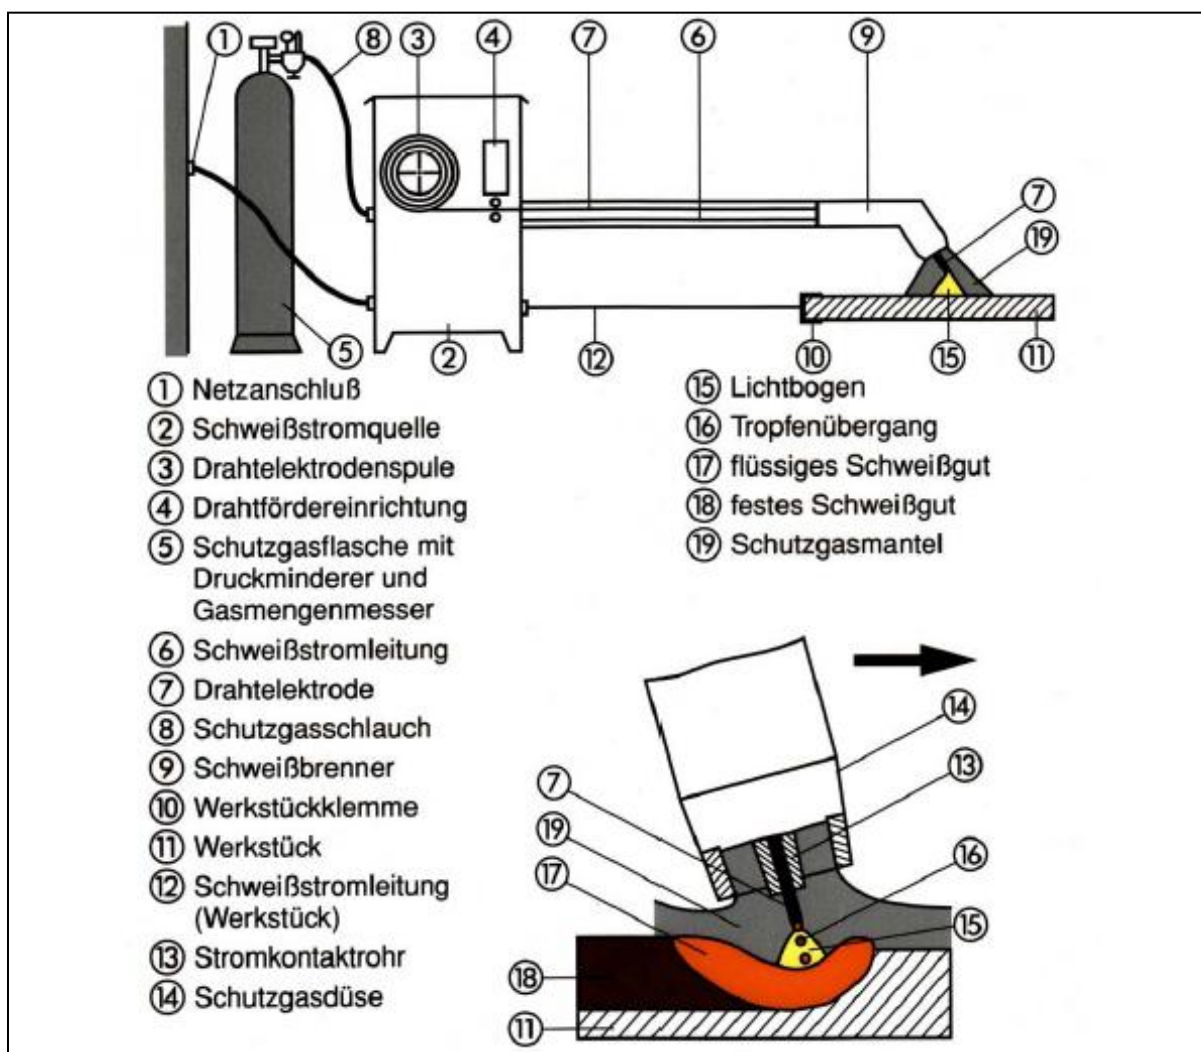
Metall-Schutzgasschweißen (MSG) MIG/MAG /²⁶/
